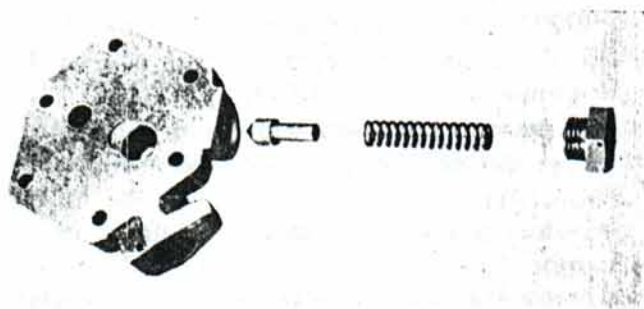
Tapa de la bomba de aceite y despiece de la válvula reguladora de presión.
